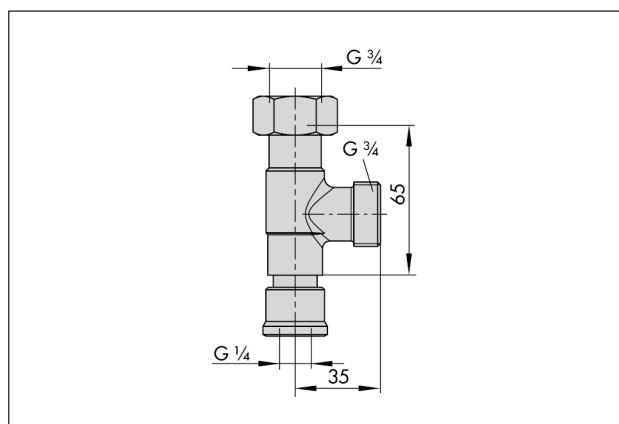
Zirkulationsanschluss (inkl. Dichtung)
